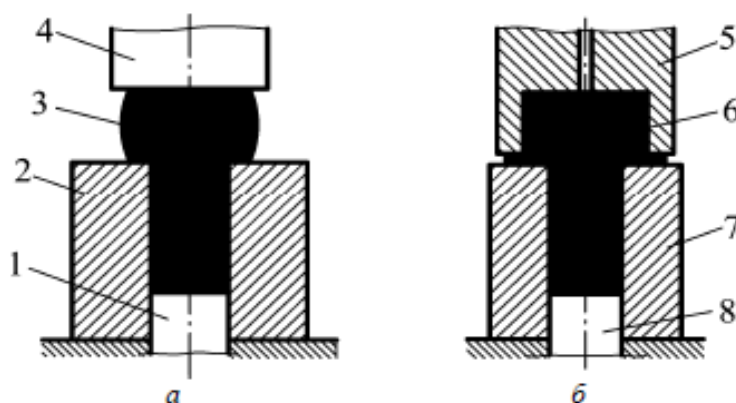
Схема высадки открытой (а) и закрытой в штампе (б): 1, 8 – выталкиватели; 2, 7 – матрицы; 3, 6 – заготовки; 4, 5 – пуансоны
